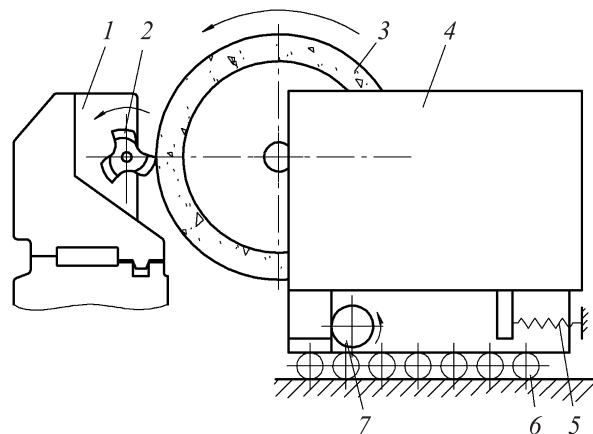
Схема затылования резьбовой фрезы на резьбошлифовальном станке модели 5822 [6, 7]
